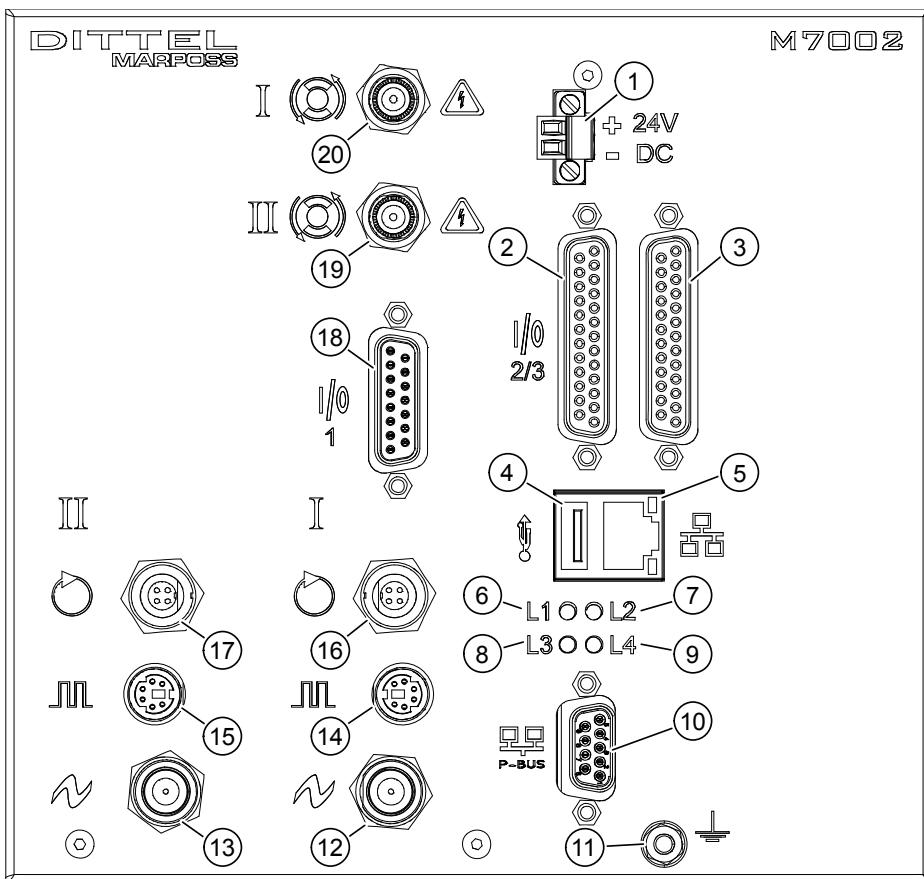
M7002 Stecker und Buchsen an der Frontseite
